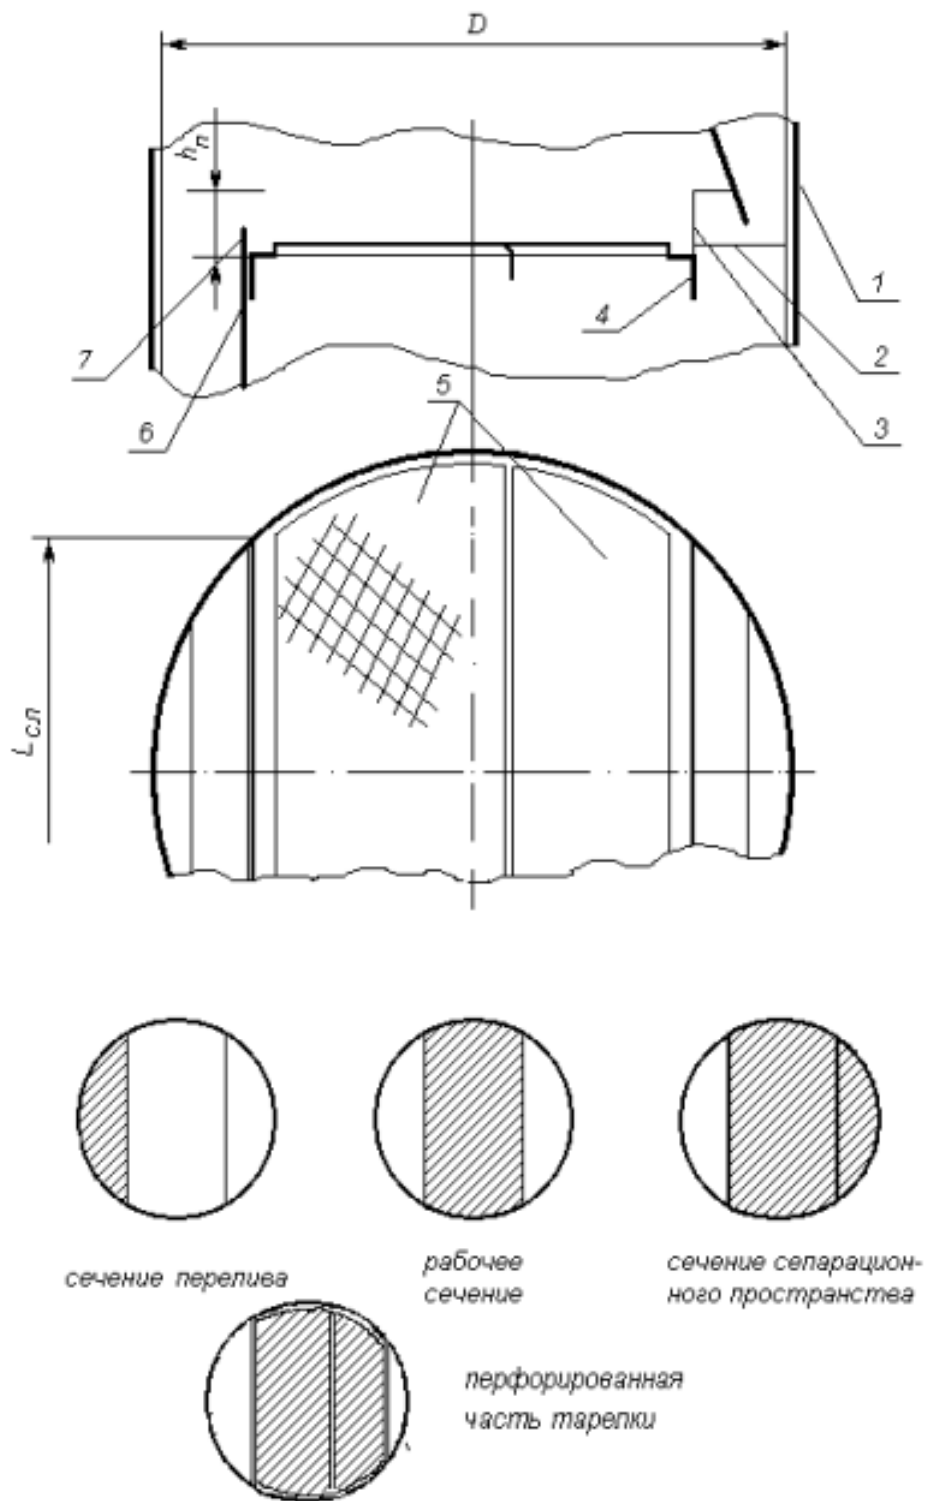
Устройство разборных ситчатых тарелок (детали крепления не показаны) : 1 - стенка колонны; 6 - сливной лист; 2 - пластина для упора сливного листа ; 7 - переливная планка; 3 - сливной сегмент; D – внутренний диаметр колонны; 4 - опорная рама;  $L_{сл}$  – длина перелива; 5 - секции тарелки;  $h_p$  – высота перелива.
